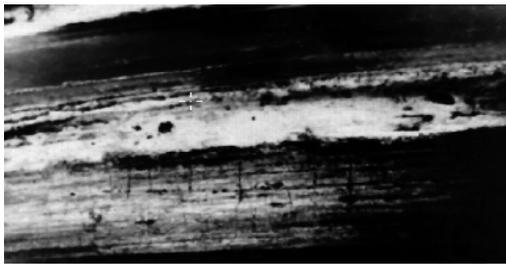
Fisuras térmicas en el centro de la rodadura
